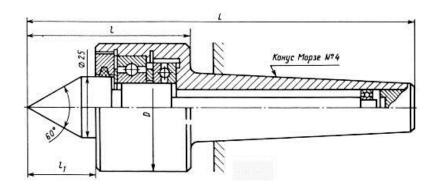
Вращающийся центр для заготовок с центровым отверстием
